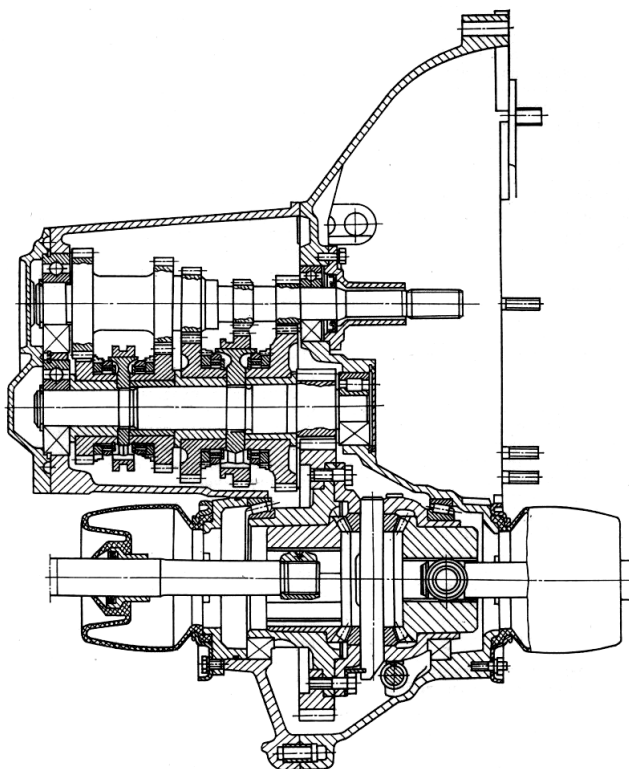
конструкция КПП переднеприводного автомобиля с поперечным расположением ДВС
